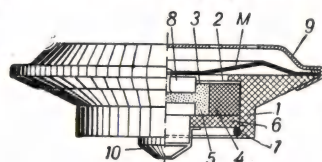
Капсальный микрофон: М — мембрана; 1 — корпус; 2 — слюдяная шайба; 3 — шелковая шайба; 4 — пластмассовые кольца; 5 — угольный порошок; 6 — шайба; 7 — пружинящее зажимное кольцо; 8 — подвижный электрод; 9 — металлическая крышка; 10 — неподвижный электрод.
